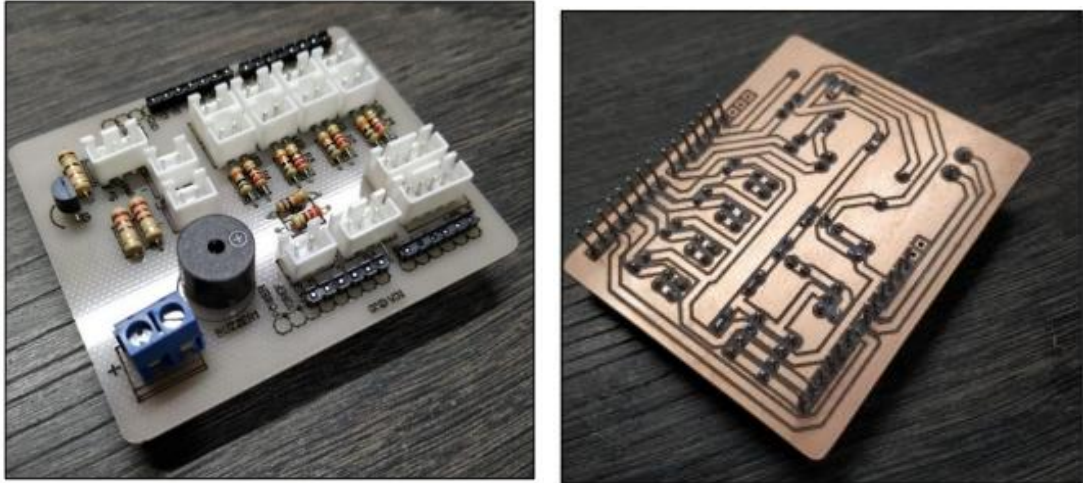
Parte superior y posterior de la PCB con componentes soldados.
